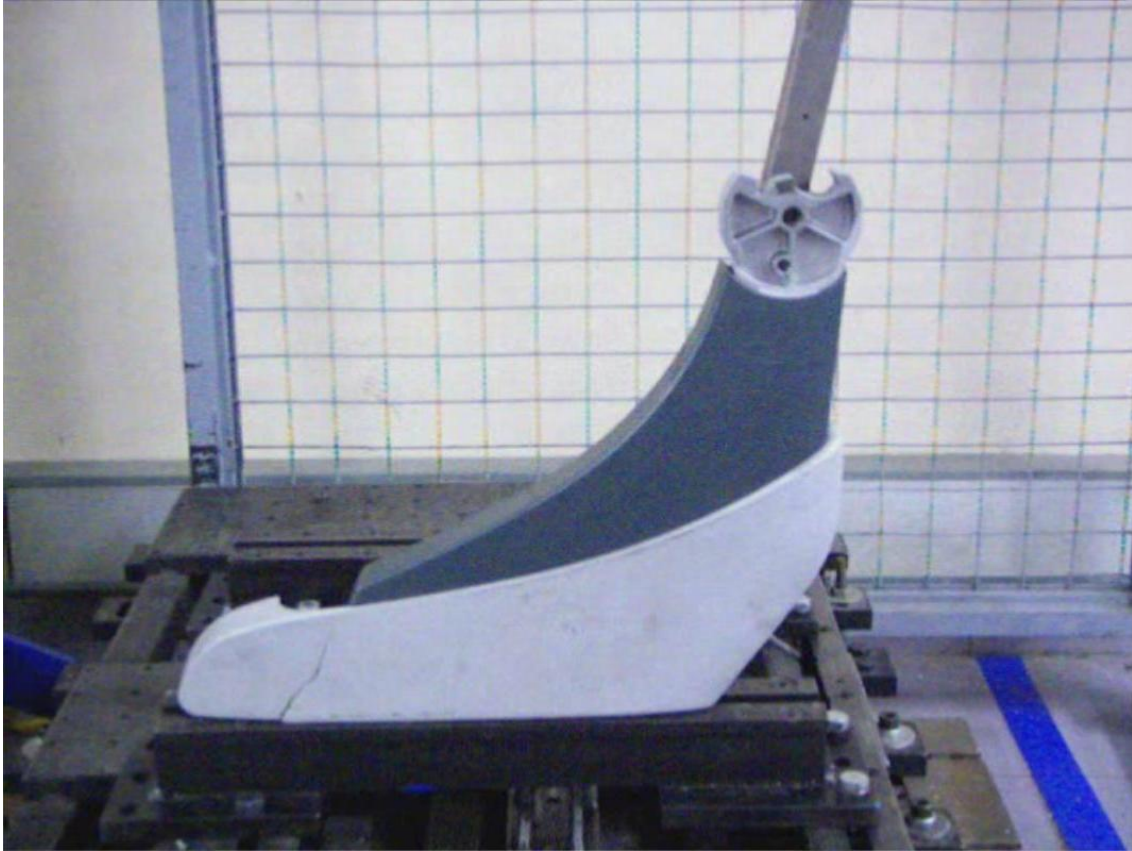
Aparición de la primera grieta en la pieza.
